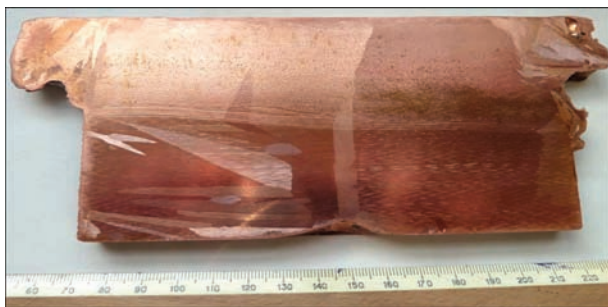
Вид осевого темплета образца, наплавленного с использованием твердого присадочного материала
